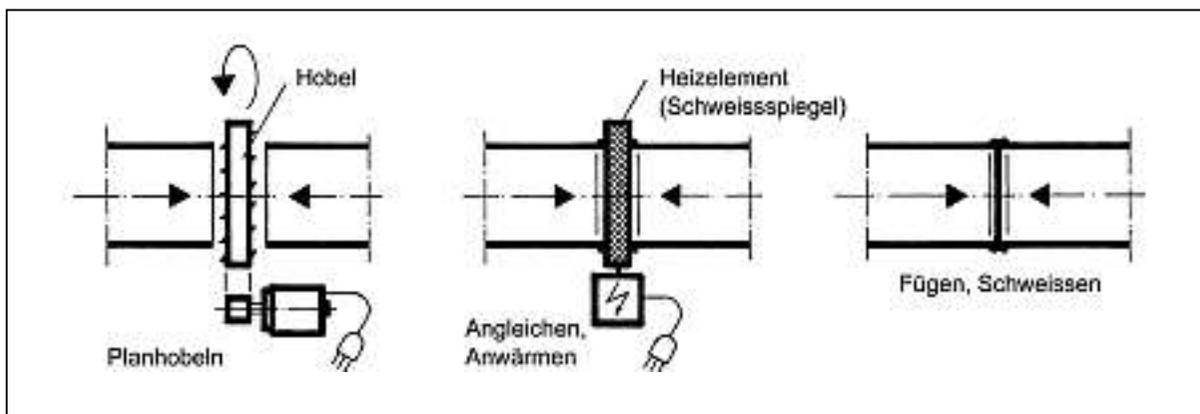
Prinzip der Heizelement-Stumpfschweissung
